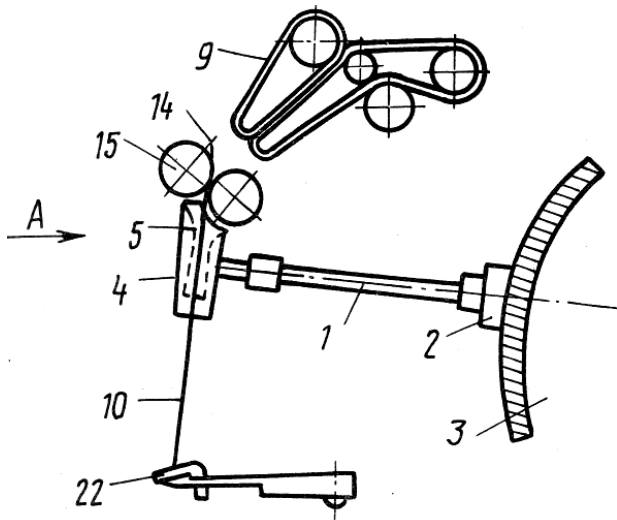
Загальна схема розміщення пристрою (вид збоку)
